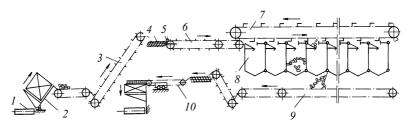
Схема установки для сортировки досок по длине и укладки их в транспортные пакеты:
